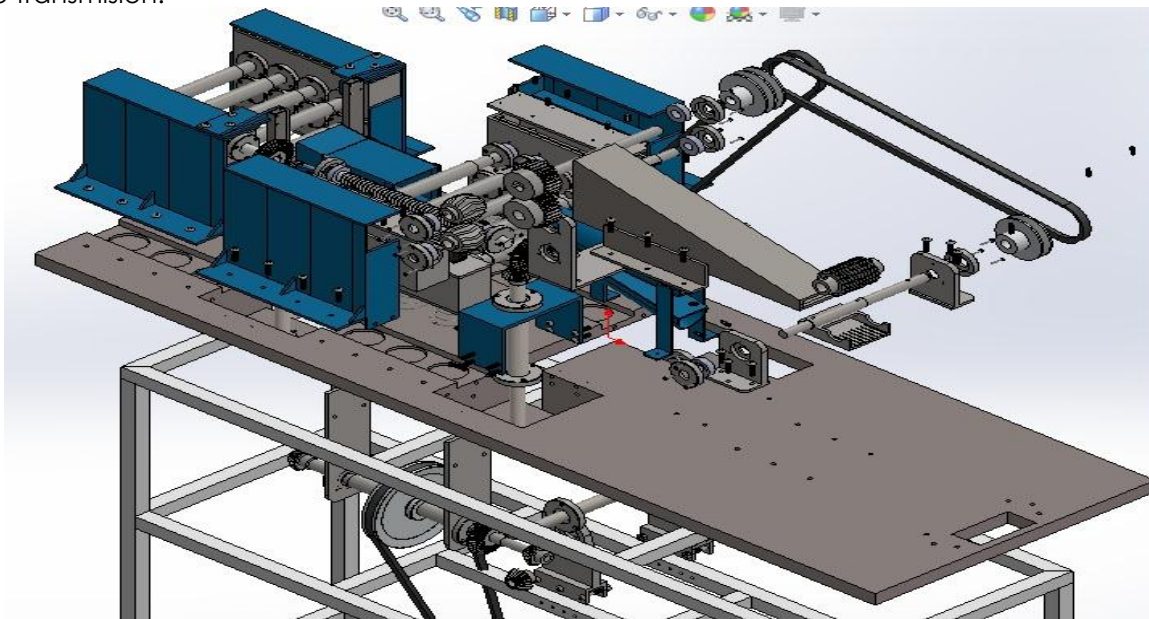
Vista explosionada de la máquina cortadora para tiras de otatillo.
